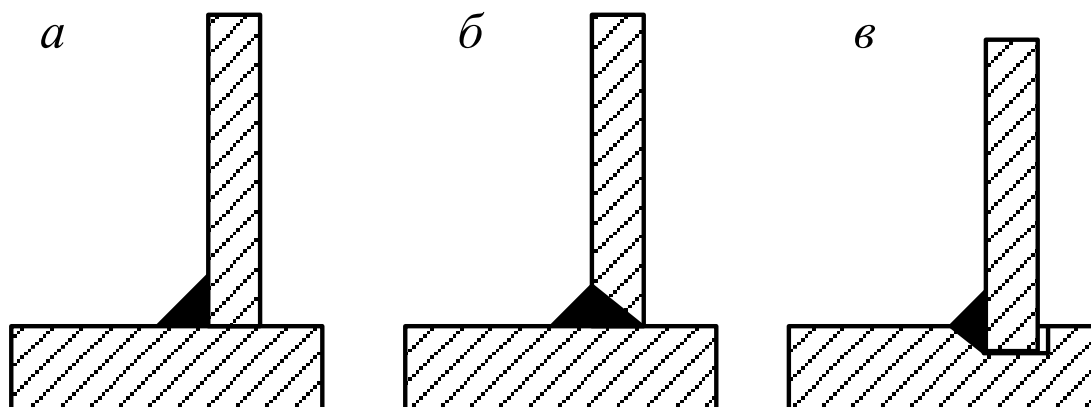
Зварні з'єднання обичайок з трубними дошками
